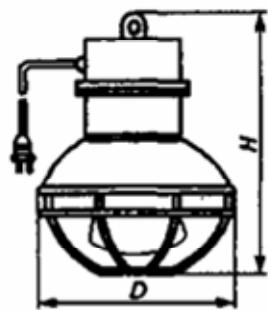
Внешний вид облучателя серии ССП10-250-010
